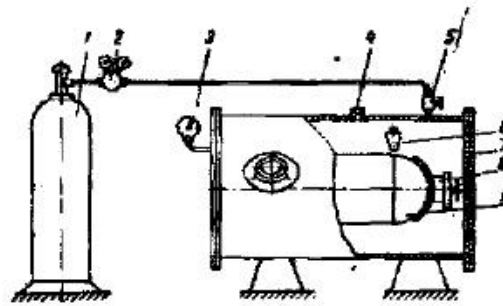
Дуговая сварка титана в камере с инертным газом 1-баллон с инертным газом; 2-редуктор; 3-вакууметр; 4-предохранительный клапан; 5-запорный вентиль; 6-сварочная головка, крышка; 8-приспособление; 9-свариваемый узел
